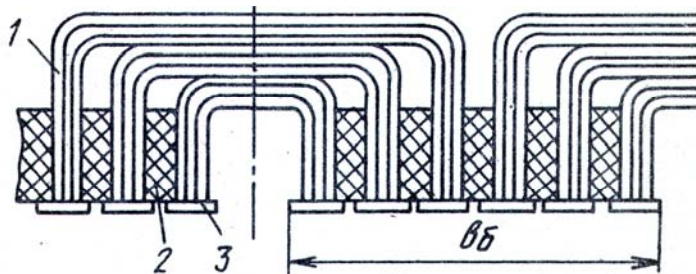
Конструкція індуктора лінійної машини постійного струму, що дозволяє звести робочий повітряний проміжок до технологічного
